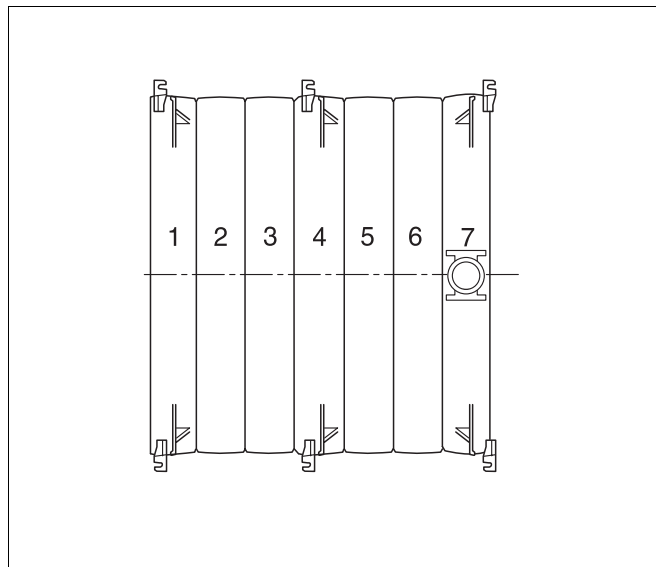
Pianta: blocco caldaia (7 elementi) con supporti
